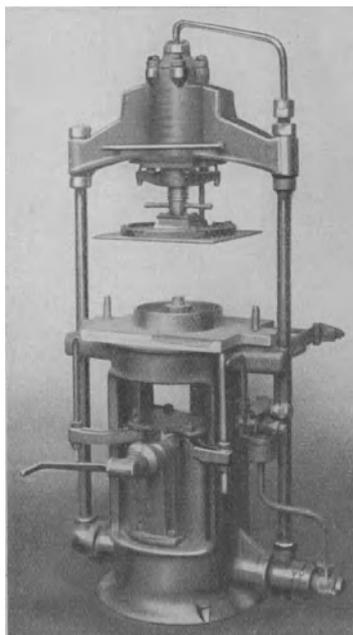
Hydraulische Abhebestift-Formpresse mit oben liegendem Preßzylinder.
